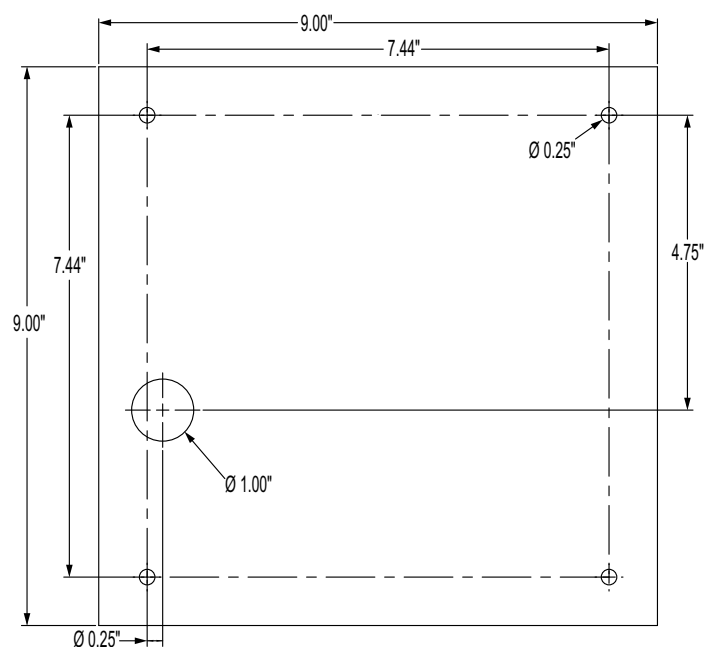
Dimensions du support de fixation pour installation à panneau - 7' po (avec clavier)
